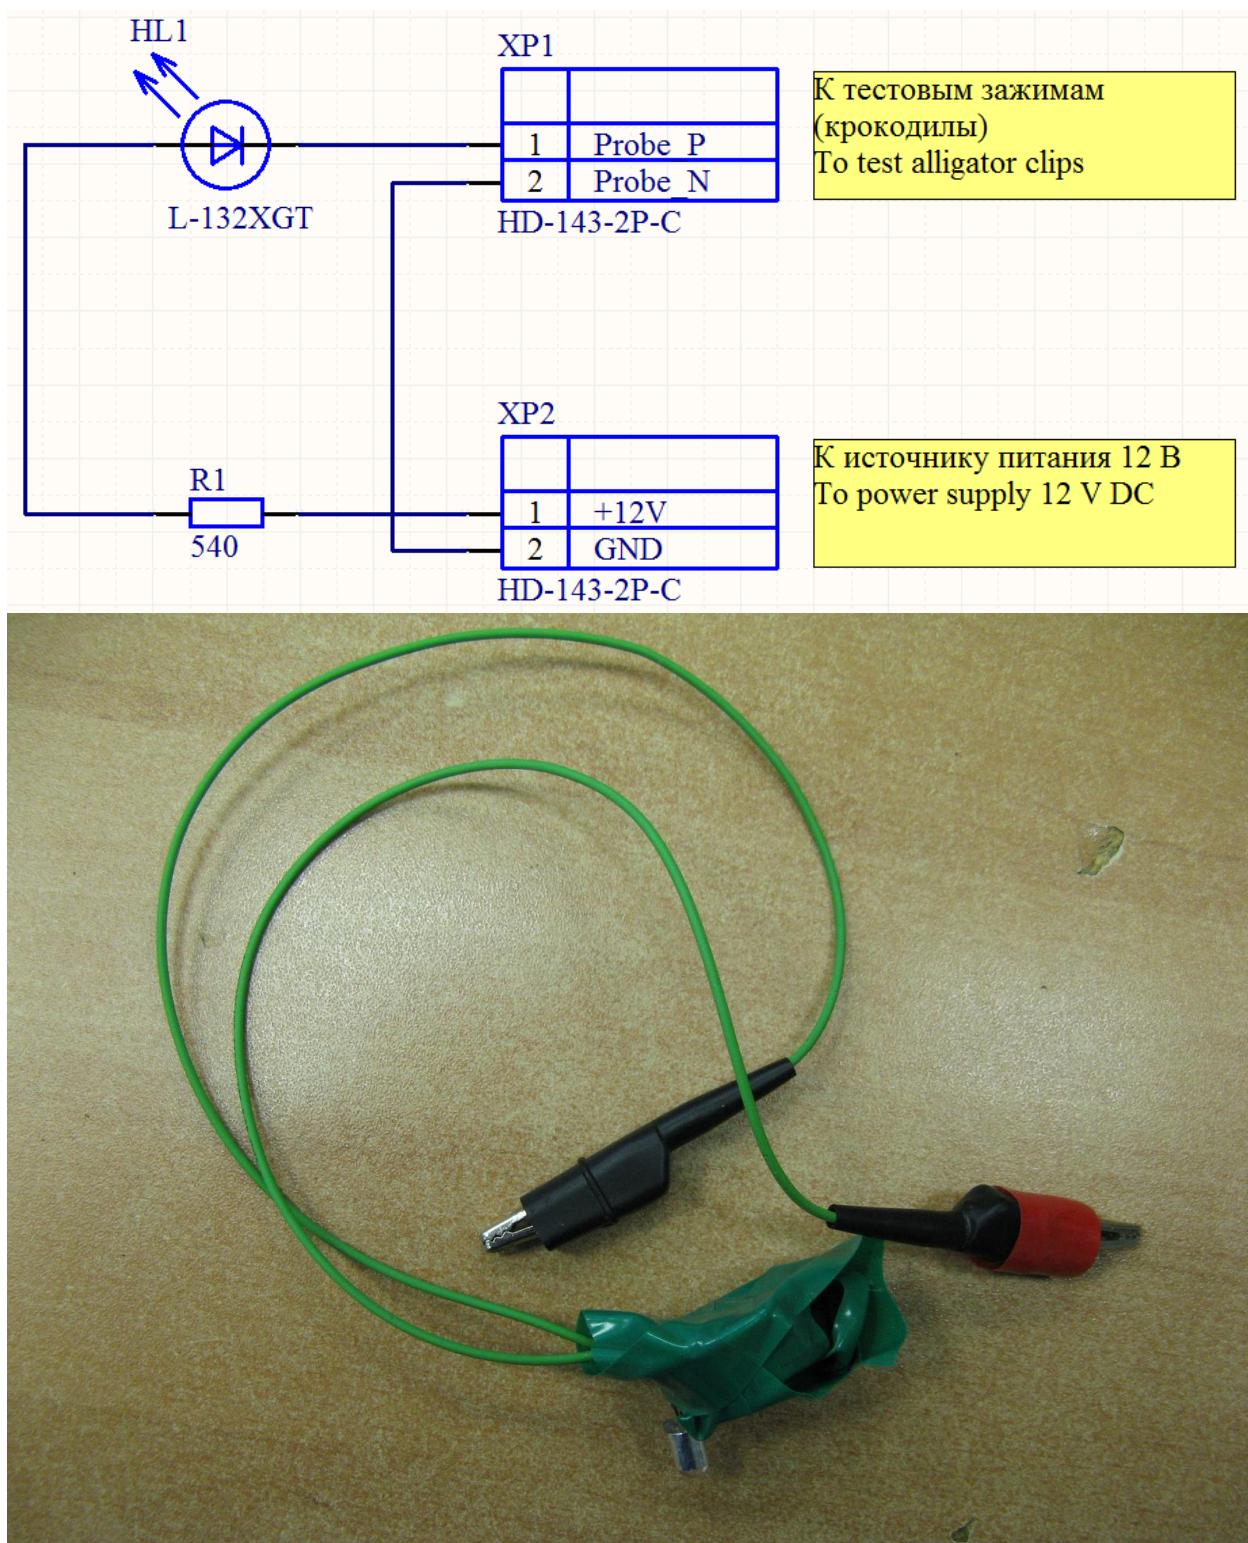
Приспособление для настройки магнитных головок EBKM.00D800.T3.00.000
